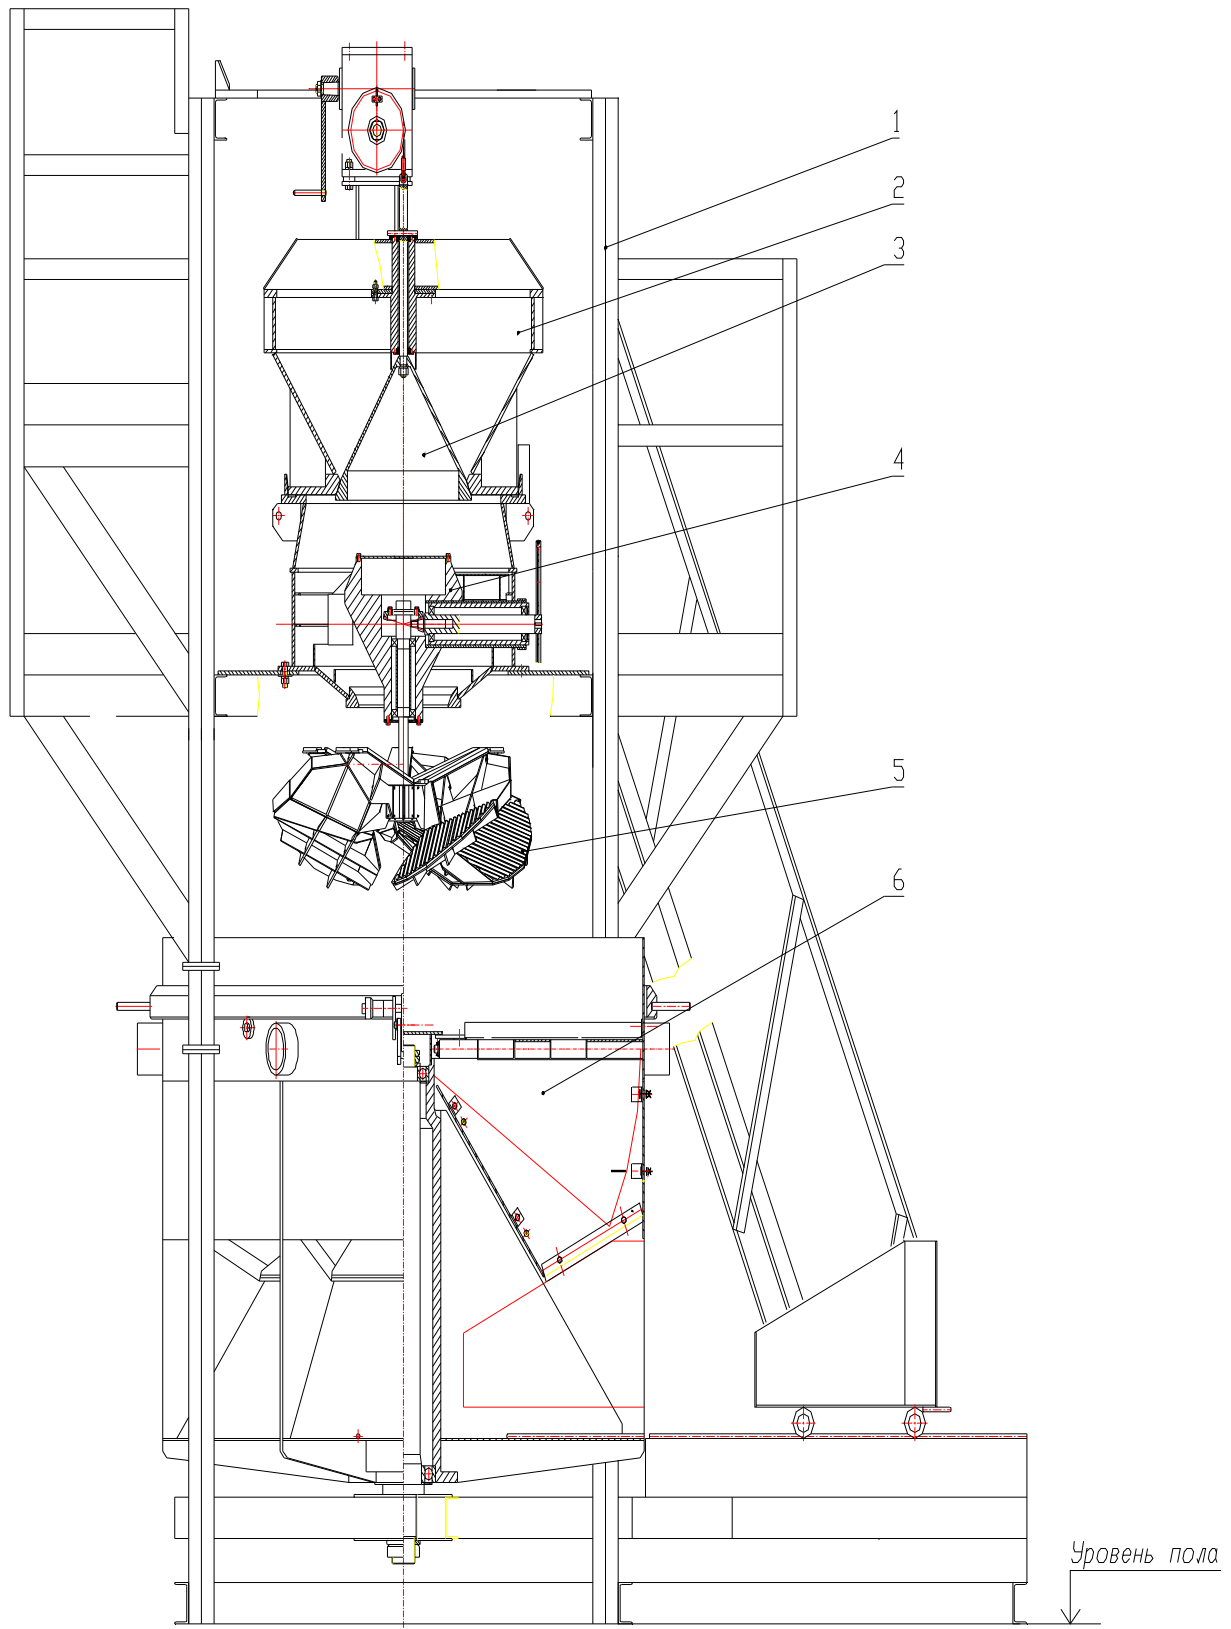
Общий вид модели роторного загрузочного устройства
